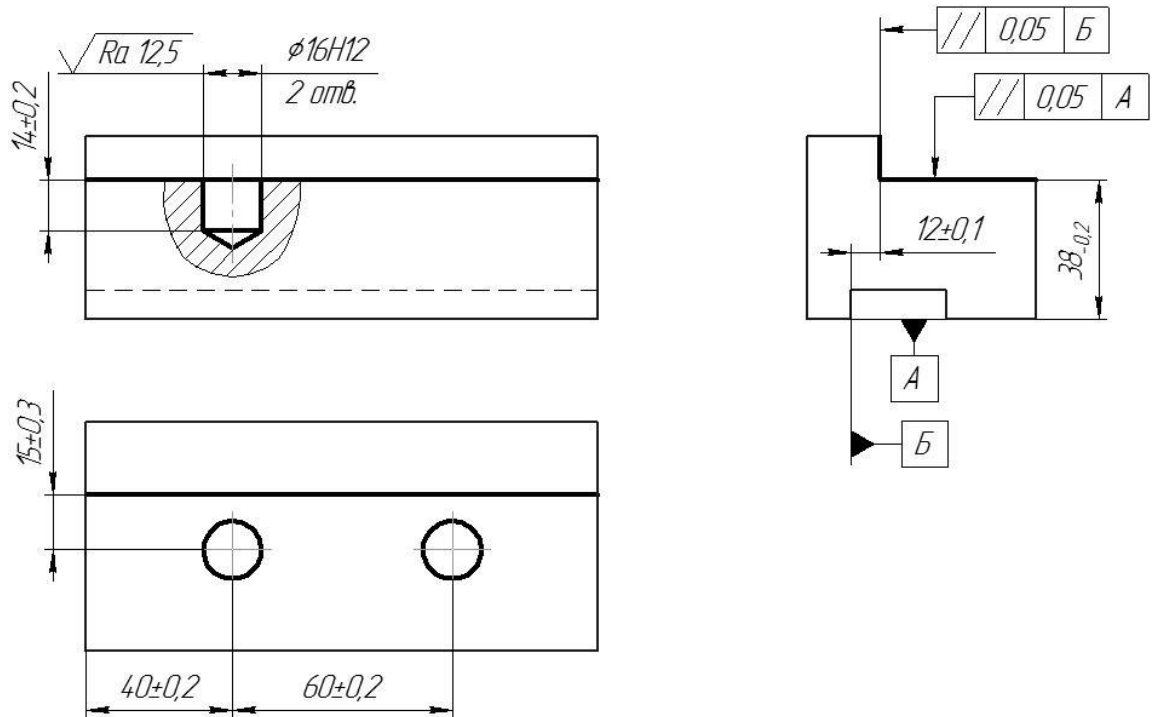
Ескіз механічної обробки поверхні деталі
